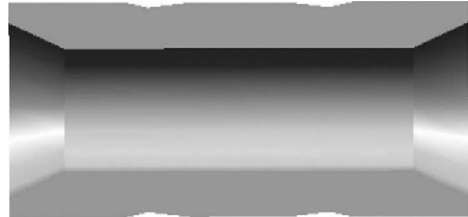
Kolbenbolzen mit Außenform (Formbolzen)
